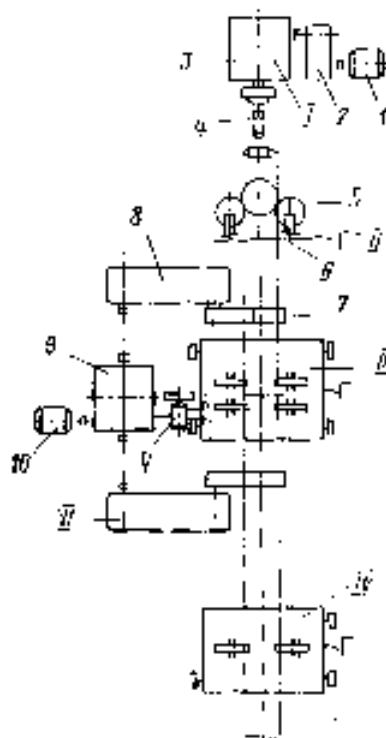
Схема механизированного сварочного стенда
